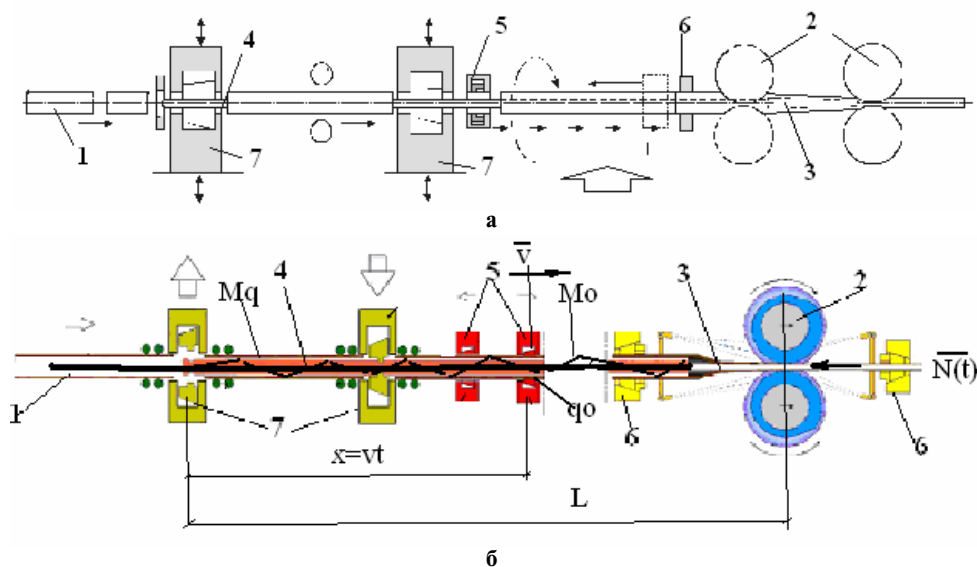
Стан холодной пильгерной прокатки труб с осевой загрузкой трубных заготовок и расчетная схема механизма удержания оправки стана ХПТ б): 1 – трубная заготовка (гильза); 2 – валки рабочие; 3 – оправка; 4 – стержень оправки; 5 – патроны подачи трубы; 6 – патроны поворота трубы; 7 – патроны удержания стержня оправки
